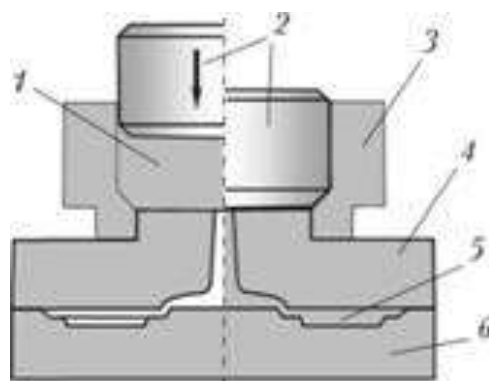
Схема ливарного пресування заготовок з пластмас:
